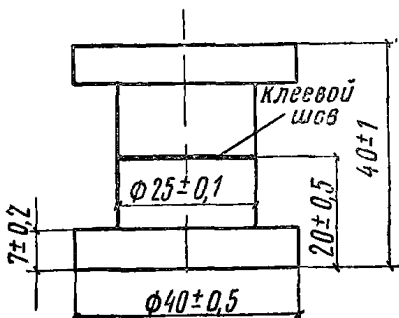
Стандартный образец для испытания клеевых соединений металлов на равномерный отрыв
